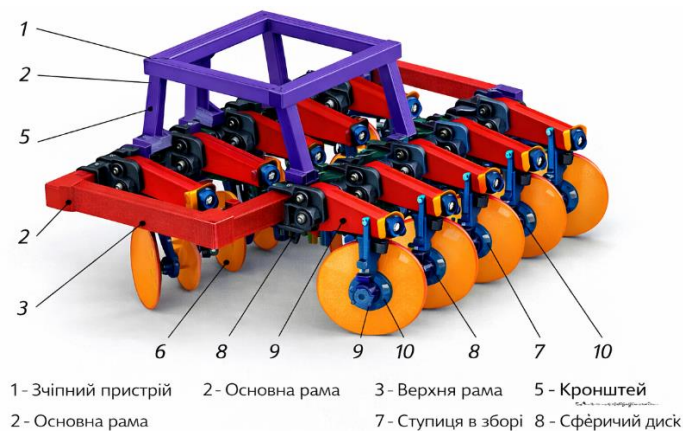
Макет культиватора виготовленний на принтері Ultimaker S3
